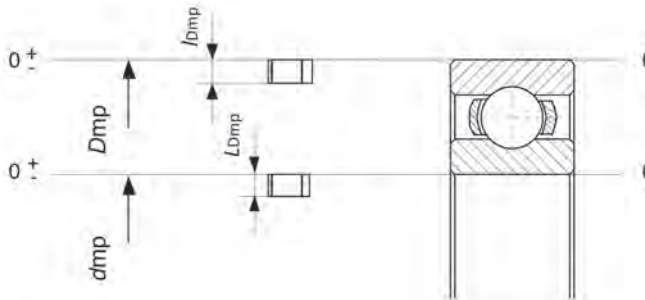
Схема общих обозначений полей допусков на средние наружный диаметр и диаметр отверстия подшипников
